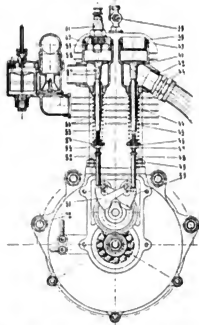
Dürckopp-Einzylindermotor, Schnitt durch die Ventilkammer.
